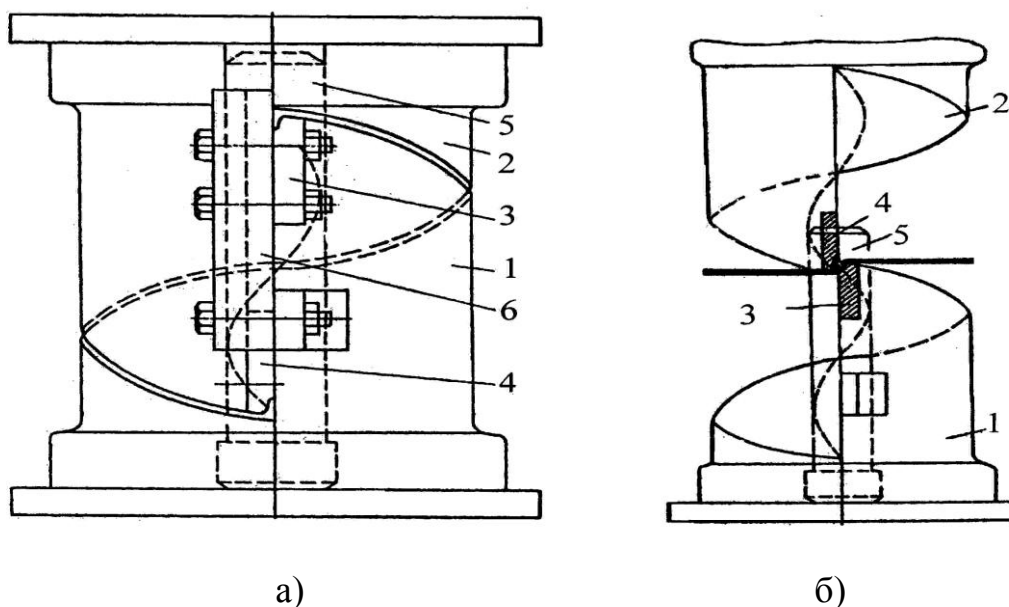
Штамп для профілювання гвинтових заготовок:
